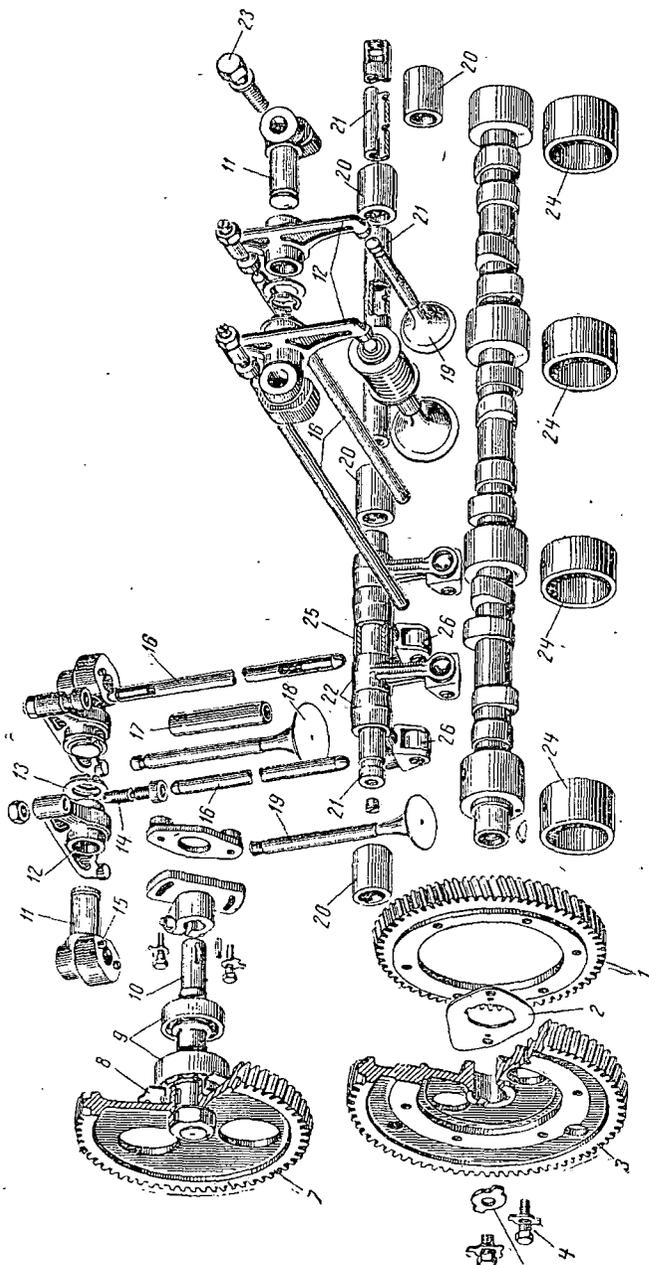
Газораспределительный механизм двигателя ЯМЗ-236:
